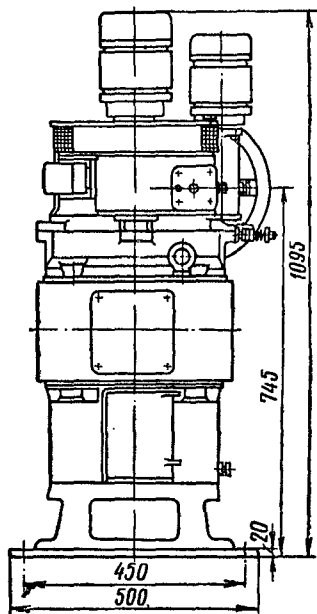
Внешний вид и габаритные размеры трехфазного индукционного регулятора напряжения
